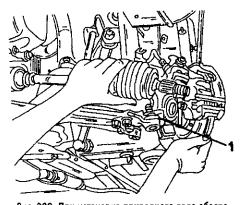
При установке приводного вала обеспечить правильное положение защитной шайбы (1) шаровой опоры.
